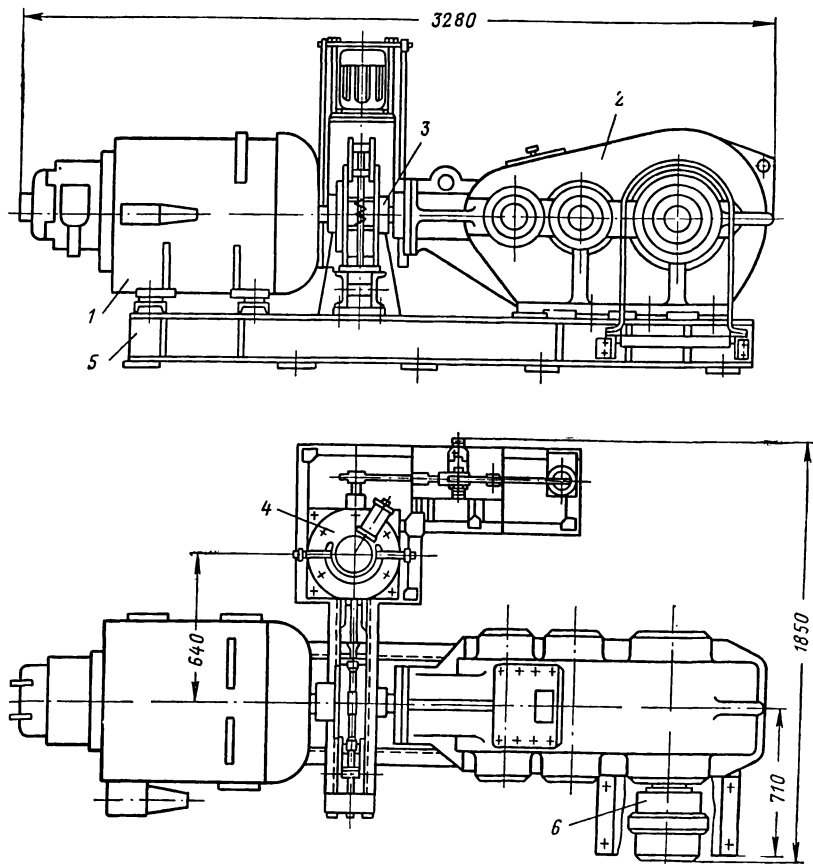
Привод конвейера с продольным расположением двигателя:
